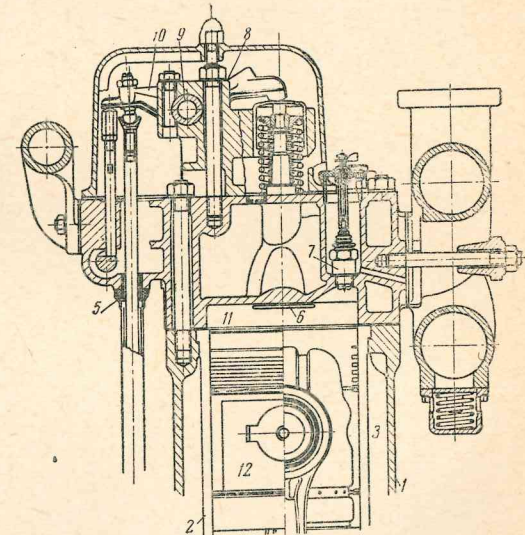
Поперечный разрез крышки газового двигателя МГС-17
